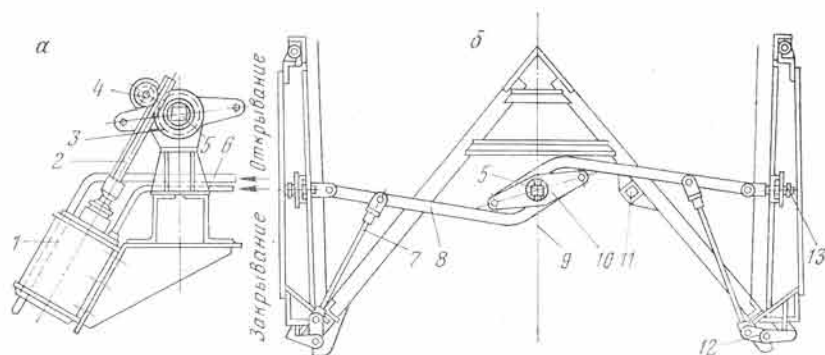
Схемы механизма пневмопривода открывания люков полувагона-хоппера:
